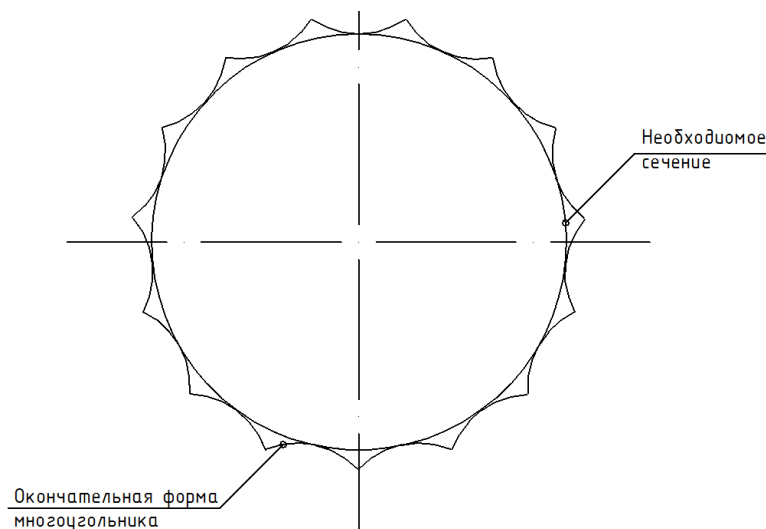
Поперечное сечение заготовки, получаемой при точении-фрезерованием
